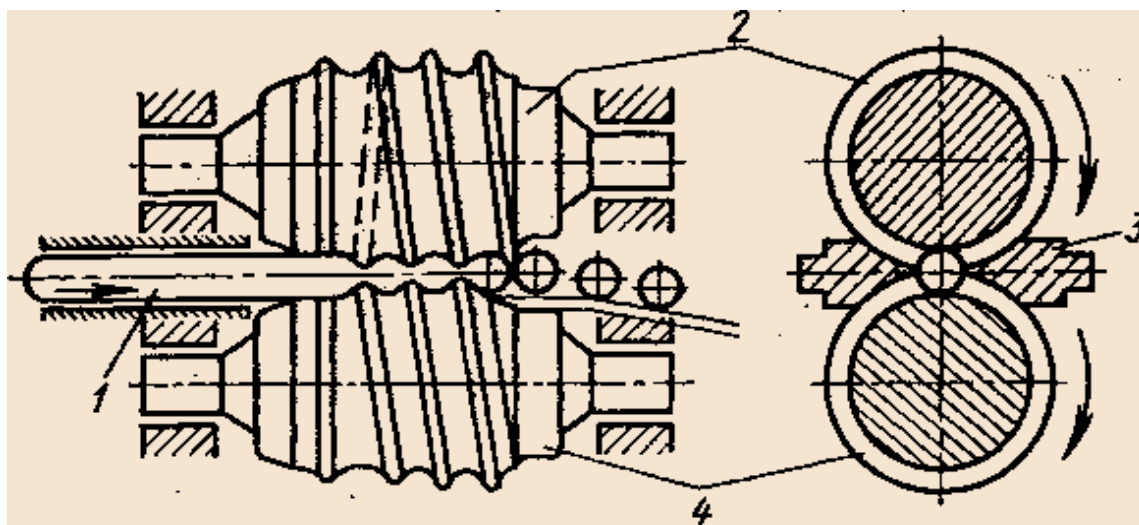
Схема прокатки шаров в стане поперечно-винтовой прокатки
